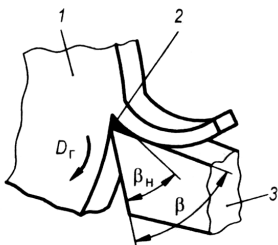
Схема утворення наросту: 1 - заготовка; 2 - наріст; 3 - різець; D_r — головний рух різання; β_n , β - кут загострення
